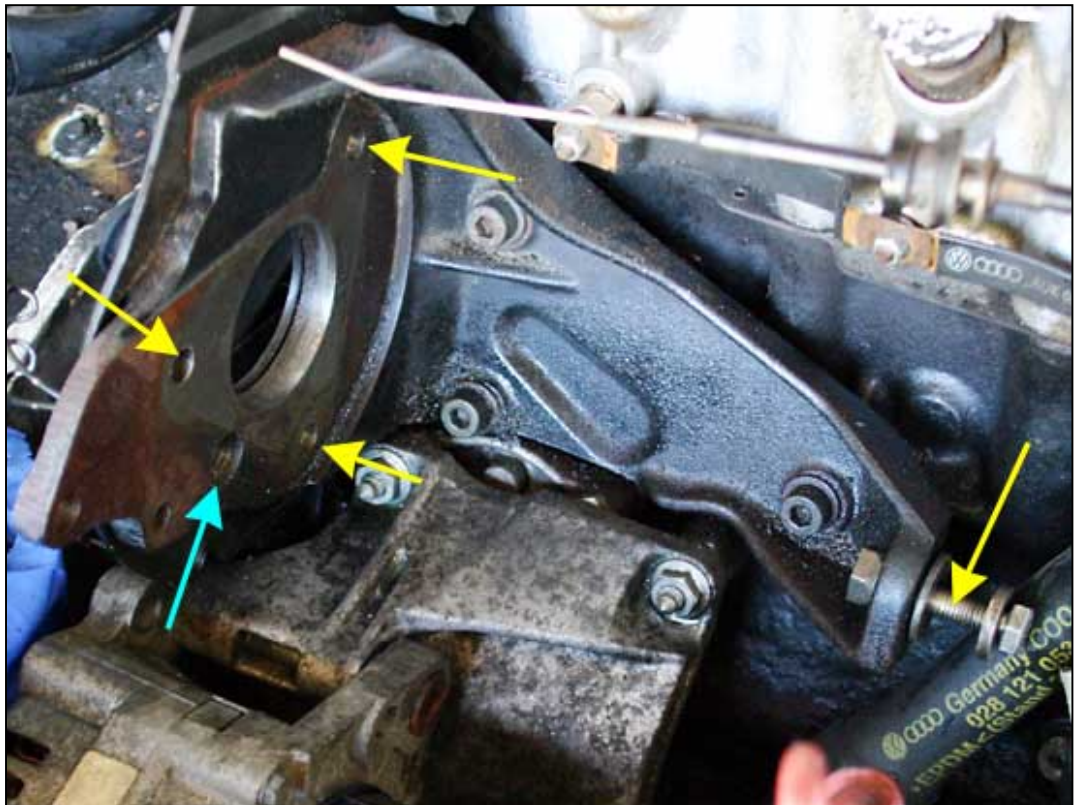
Die ESP ist draußen, Befestigungsstellen und Loch für Absteckdorn
